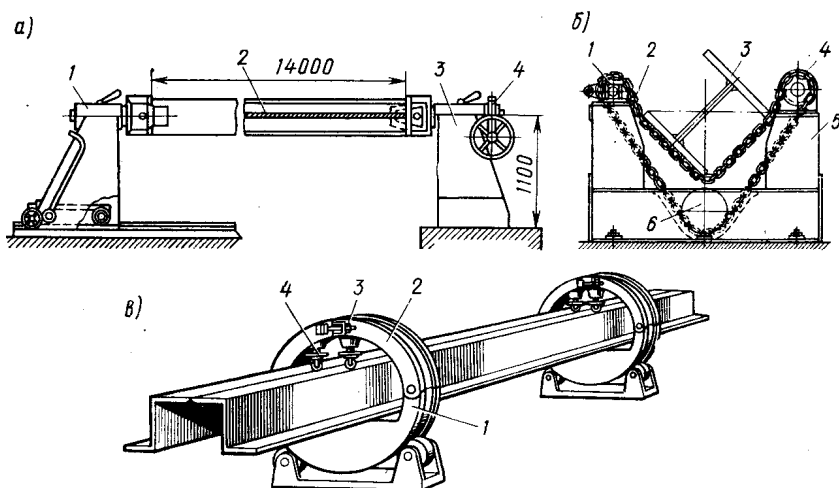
Схемы позиционеров-кантователей для сварки балок:
